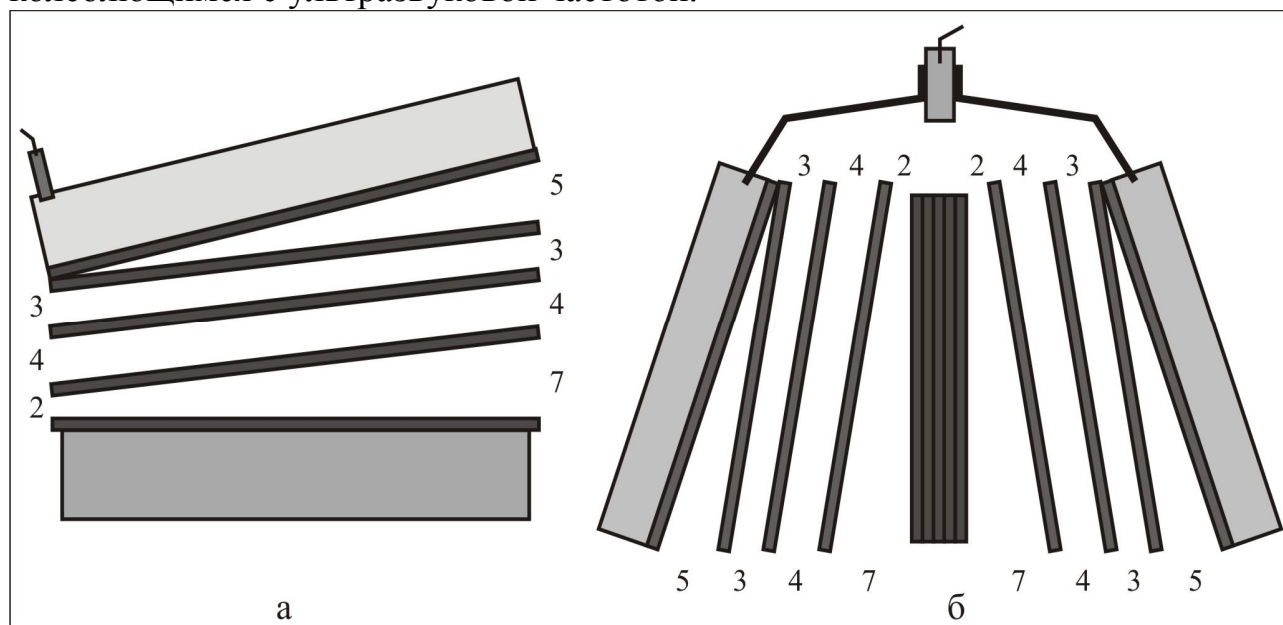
Схема получения тринадцатислойного композиционного материала методом сварки взрывом пластин из стали 20: а - этап получения пакета из 5 пластин; б - этап соединения пятислойного пакета и боковых комплектов из четырех пластин, цифрами показано расстояние между пластинами в миллиметрах.
